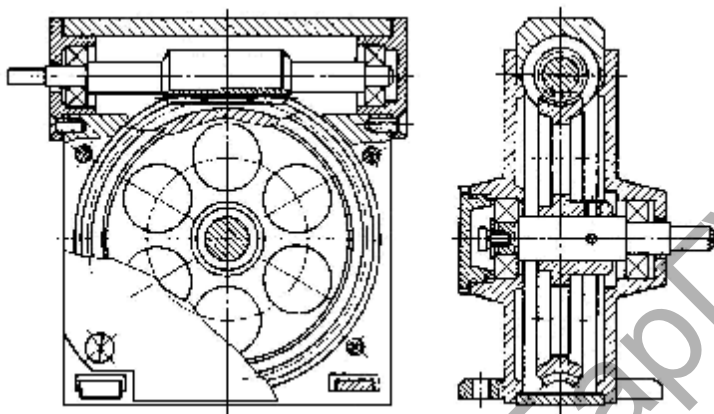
Конструкция червячного редуктора с корпусом, выполненным механической обработкой [39]
